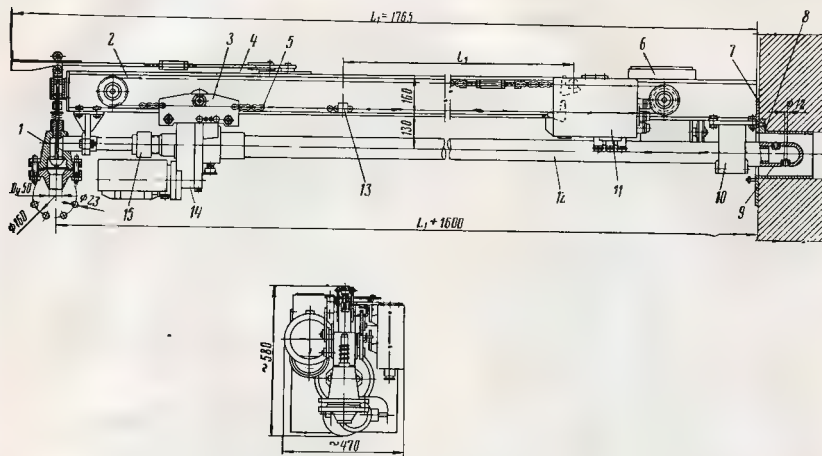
Обдувочный аппарат для пароперегревателя типа ОПК-8-59:
